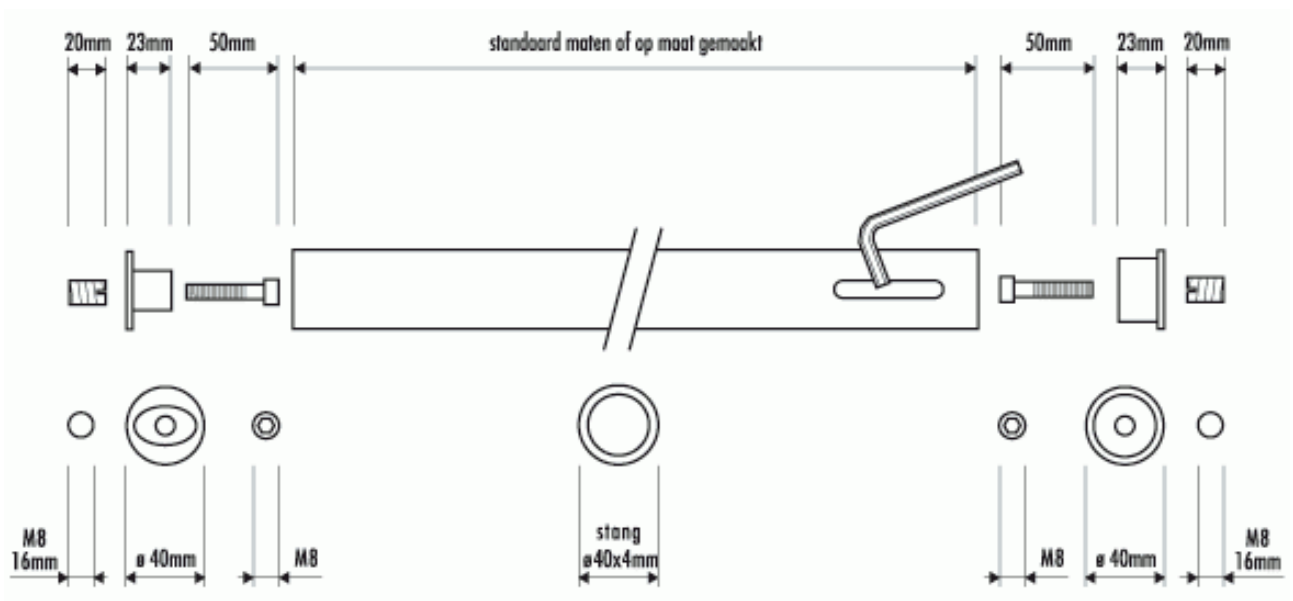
B.6 Voorgeschreven type doorvalbeveiliging met verborgen montage
